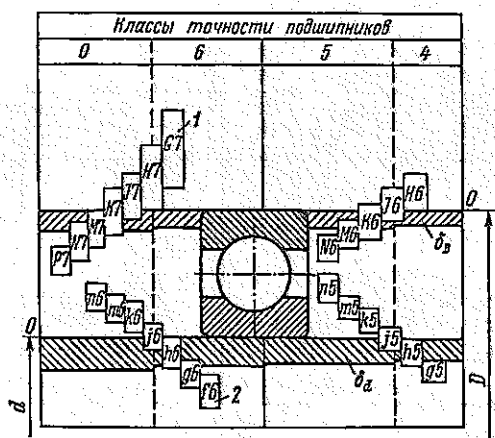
Схема полей допусков колец подшипников качения, вала и отверстия при различных посадках:
